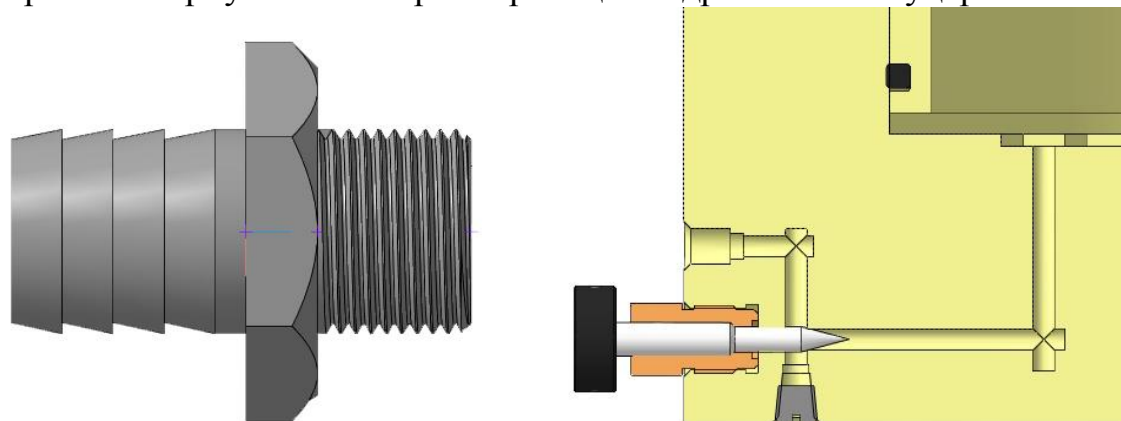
Цилиндрический штуцер и цилиндрическое отверстие в корпусе капилляриметра
